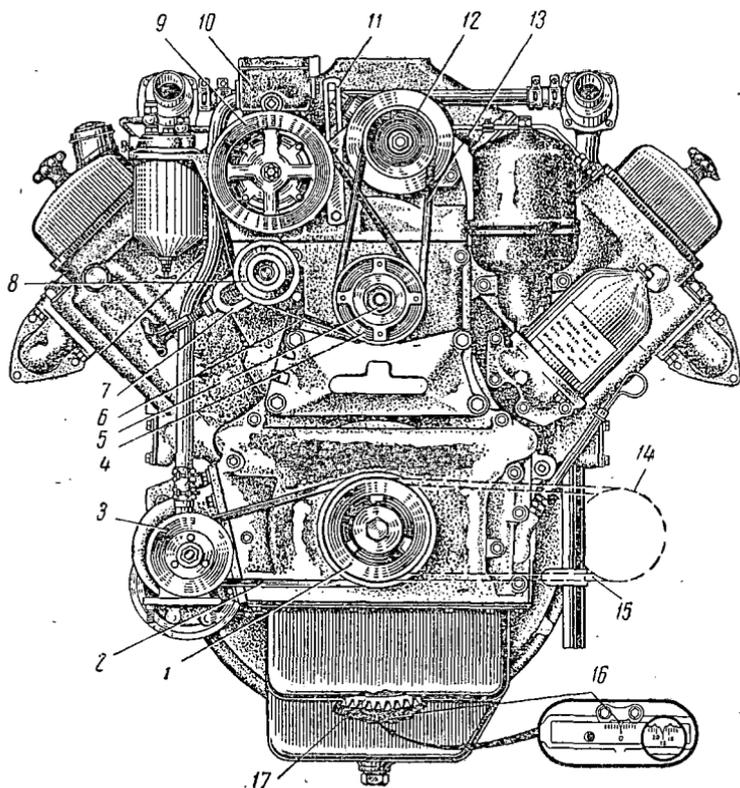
Приводы механизмов двигателя ЯМЗ-236:
